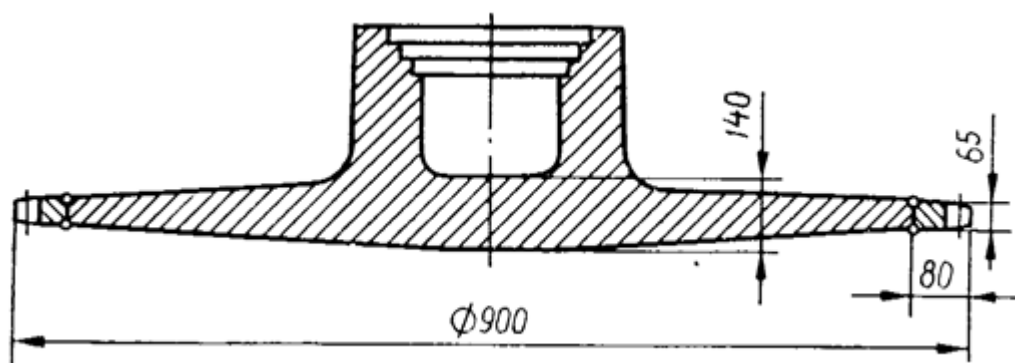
Сварной вариант ротора газовой турбины.
